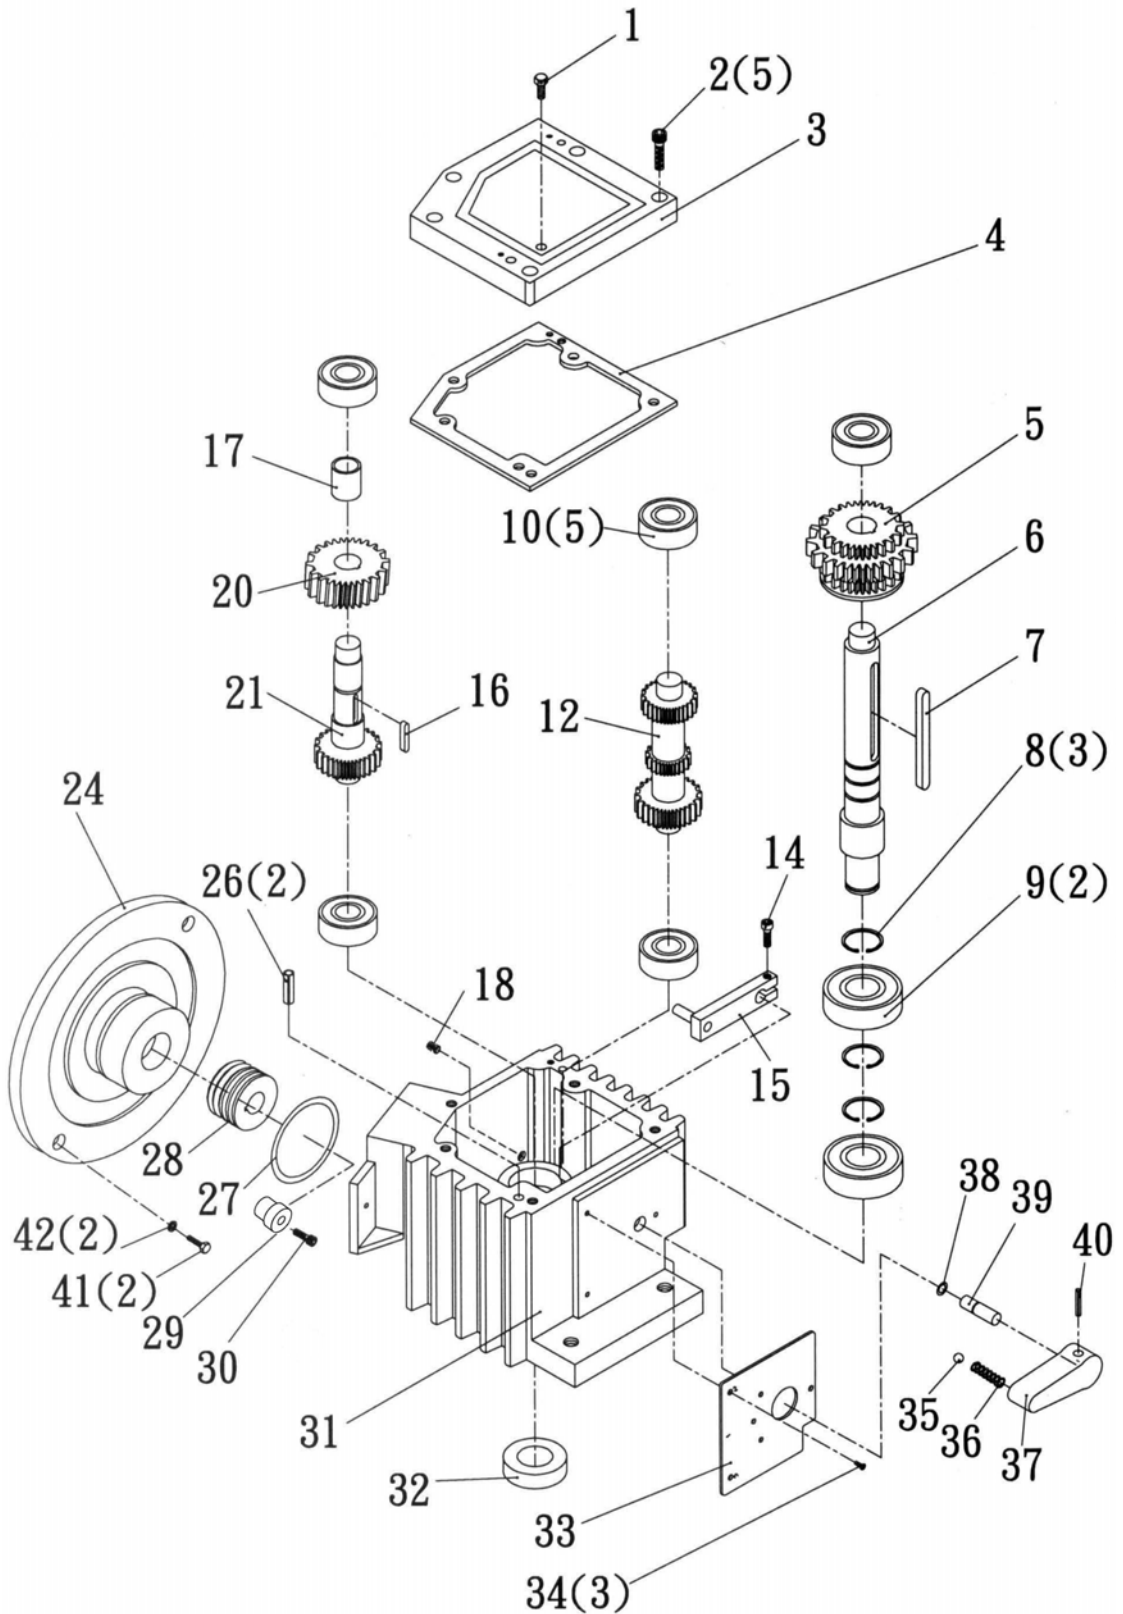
Explosionszeichnung Getriebe - Explosion drawing gear: 712AGN second generation
